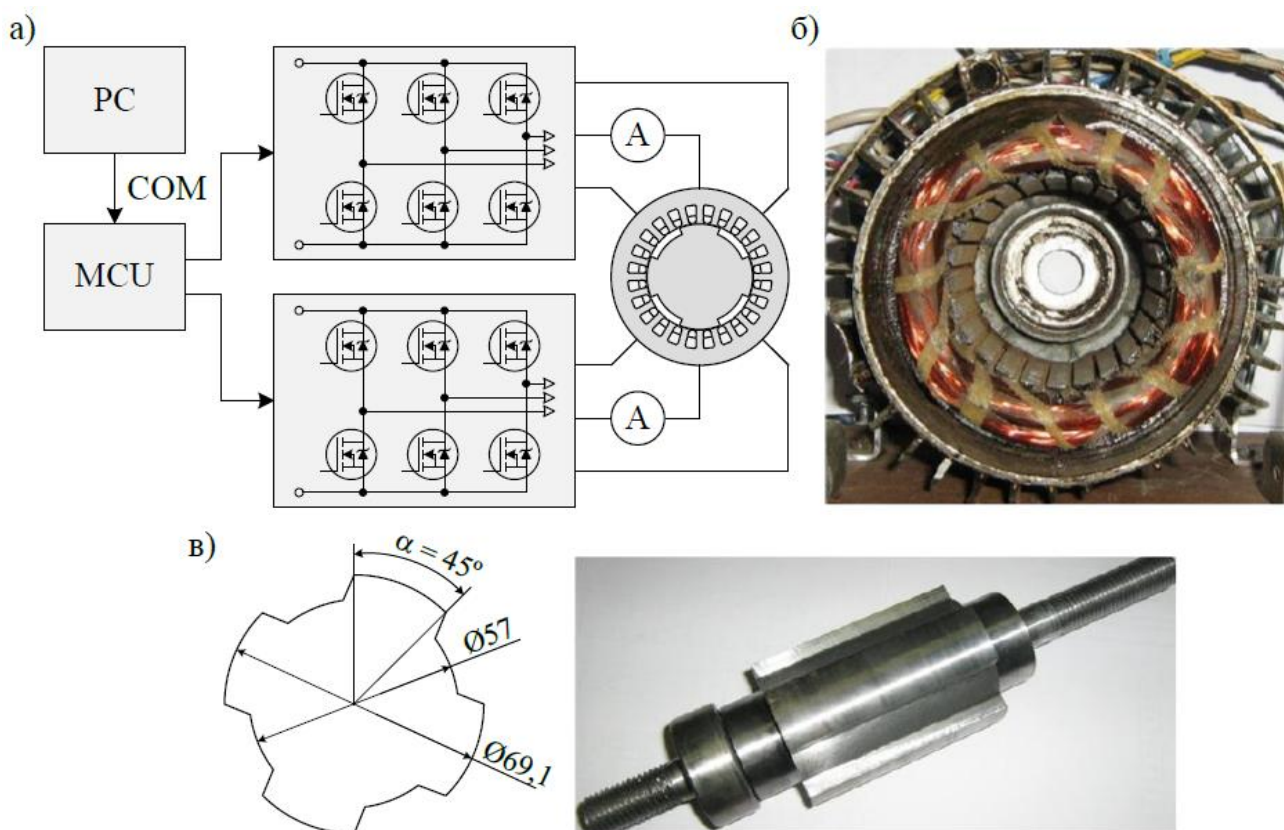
Макет СИБМ: а) функциональная схема установки, б) внешний вид статора, в) размеры и внешний вид ротора
